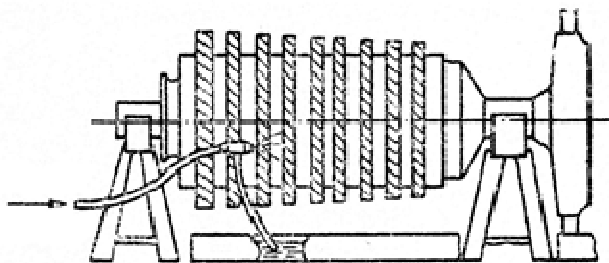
Схема очищення ротора осевого компресора: 1 – ротор компресора; 2 – опори; 3 – резервуар з сумішшю води з маршалітом; 4 - сопло
